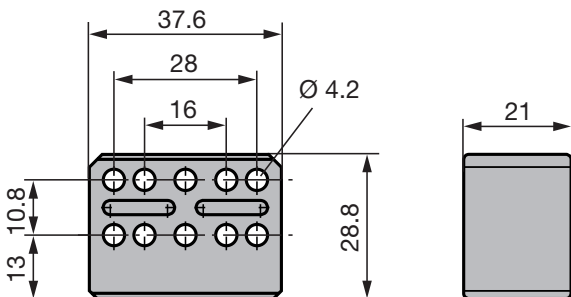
Dimensions de montage du capteur de position BTL6-A-3800-2
